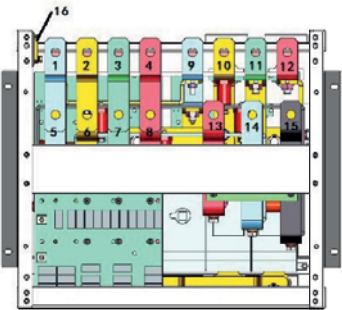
Верхняя схема электропроводки силового кабеля шкафа 300 кВА
